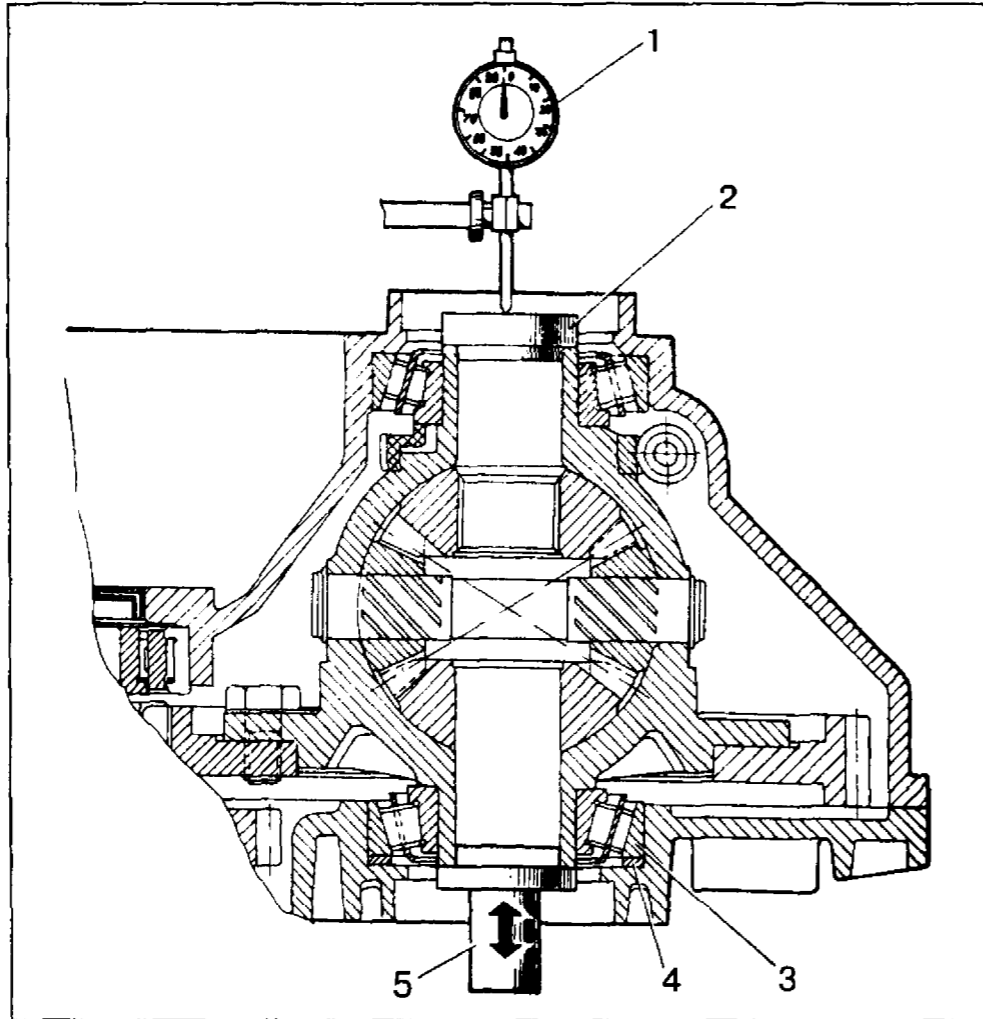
Схема подбора толщины регулировочного кольца подшипников дифференциала:
